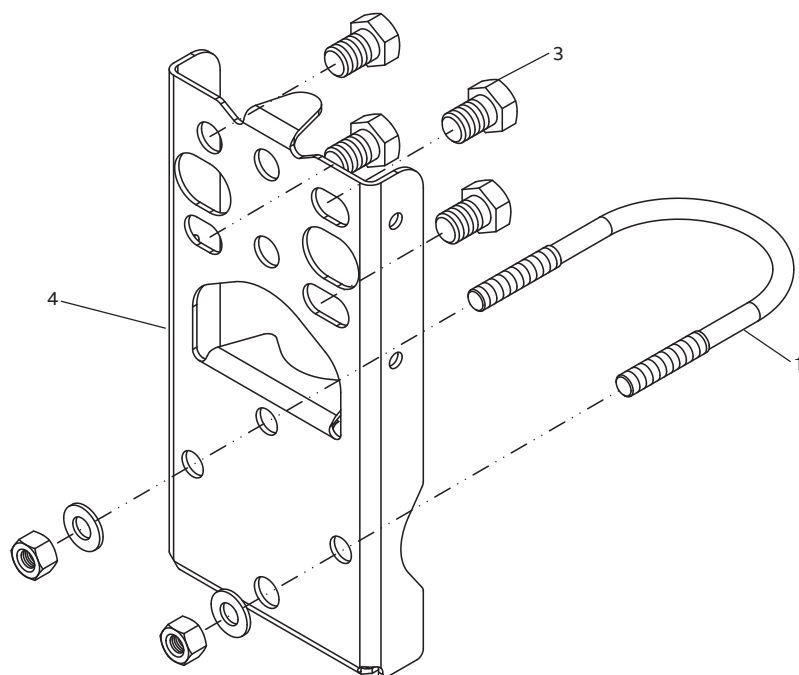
Измерительный преобразователь дифференциального давления с цилиндрическим корпусом, установленный на трубе с муфтой с помощью опционного кронштейна для нержавеющей корпуса (B5)
